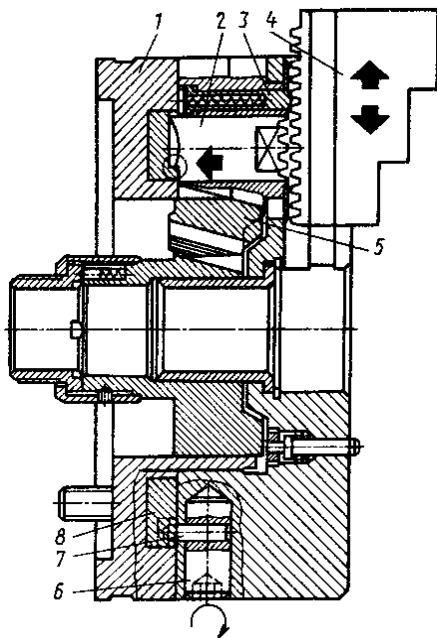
Патрон швидкопереналагоджуємий клиновий
